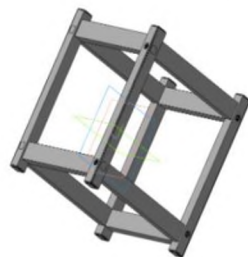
Спроектированный корпус разрабатываемого макета конструкции CubeSat
